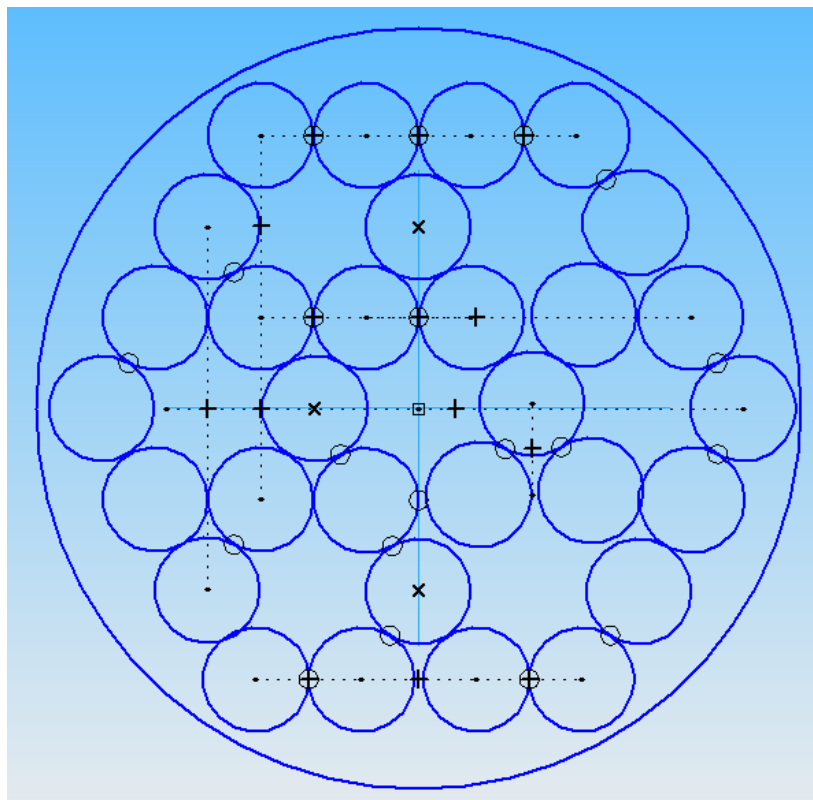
Projeto de Arranjo de Tubulações para construção de Retificador de Fluxo Tipo C adaptado para arranjo colméia.
